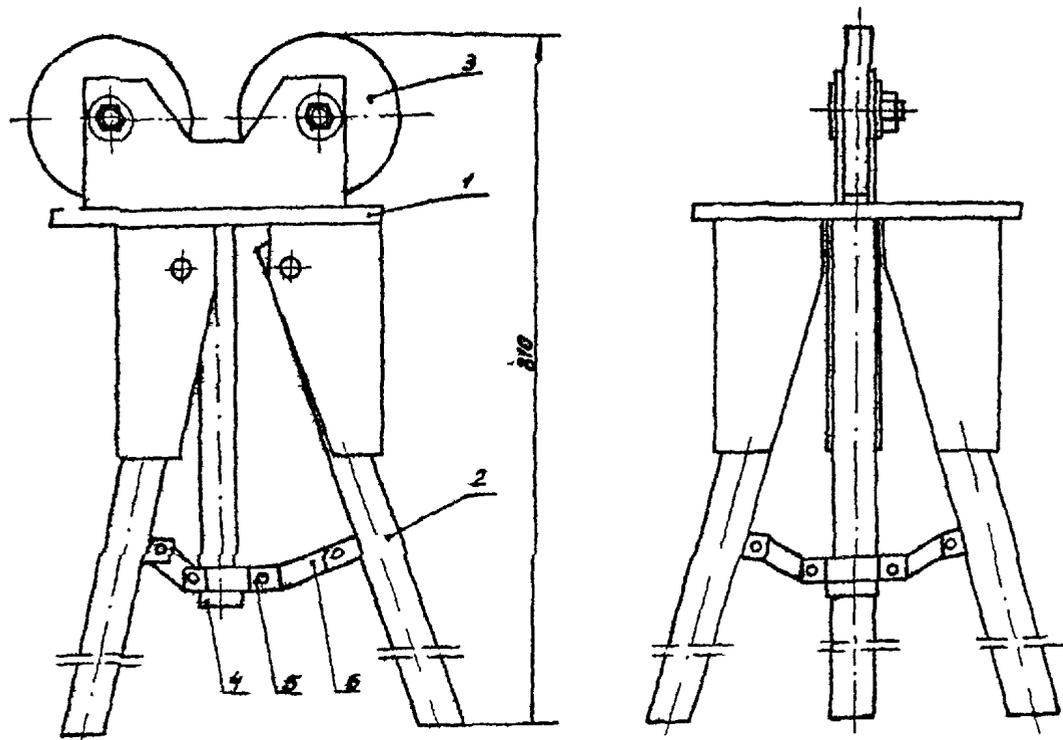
Подставка для укладки деталей тормозной системы: 1 - основание; 2 - ножка;
